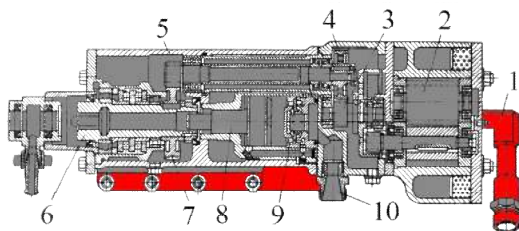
Бурильная головка 1100-1-1М (БУ-1): 1 – патрбок; 2 – шестеренчатый пневматический двигатель; 3, 4, 5, 7 – шестерни; 6 – бокса; 8 – поршень-ударник; 9 – пневмоударник; 10 – патрбок
